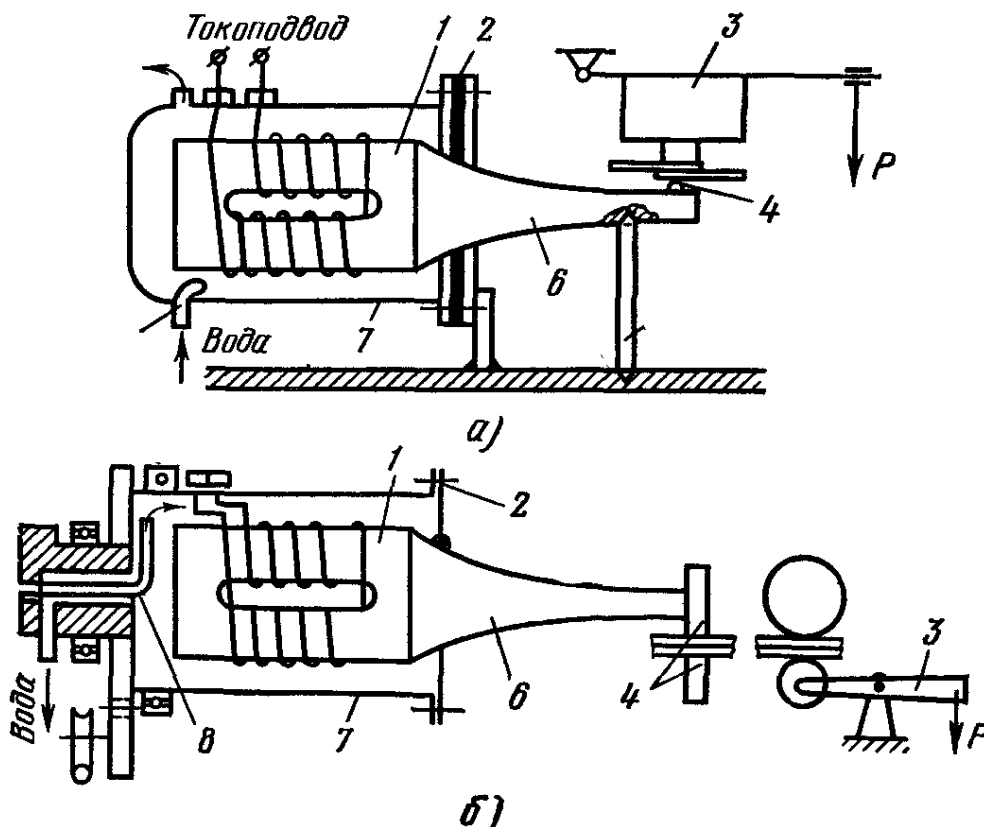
Установки для ультразвуковой точечной (а) и шовной (б) сварок:
